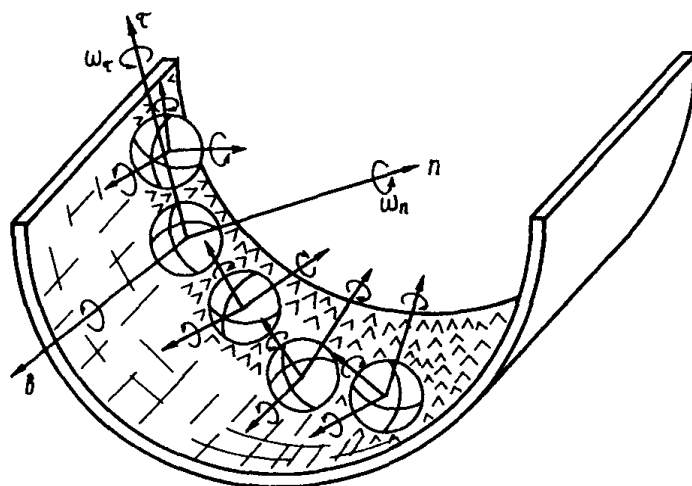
Схема пневмоцентробежной обработки и основные движения деформирующих элементов
